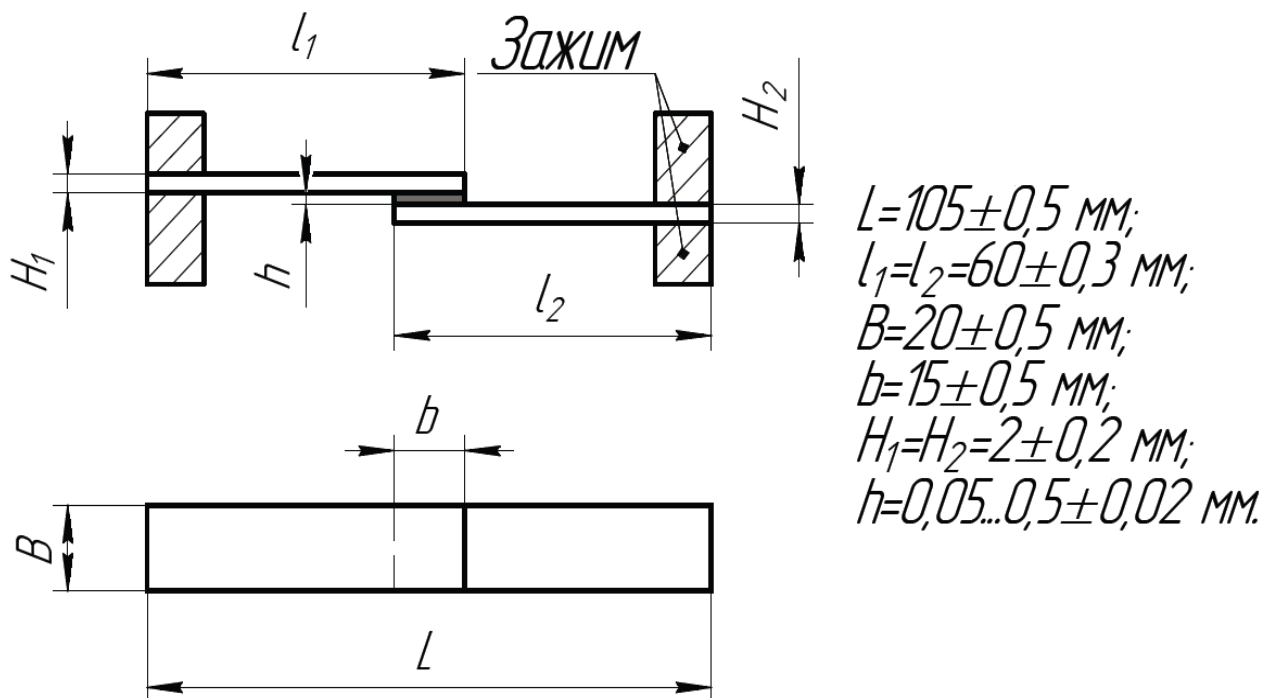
Общий вид подготовленного для испытаний образца с указанием геометрических размеров
